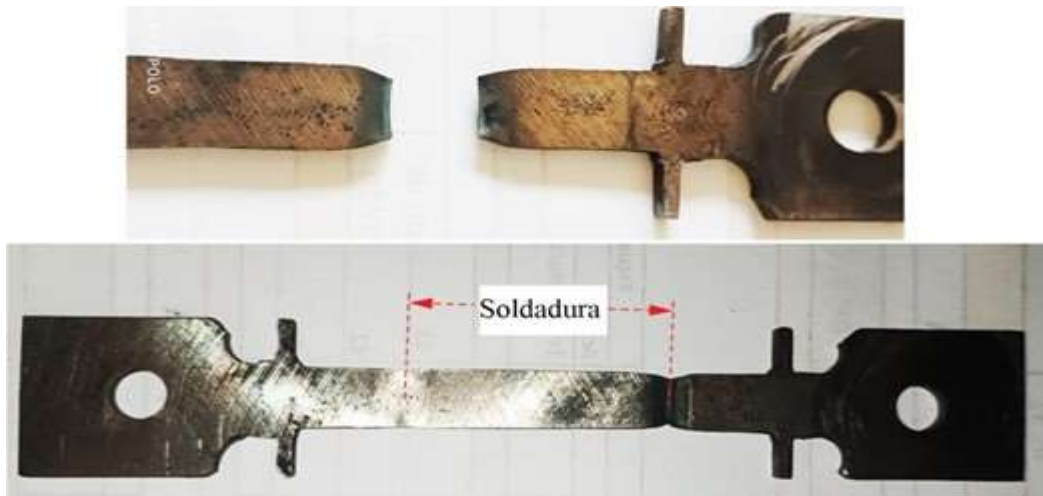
Tratamiento térmico post soldadura de 3 h a 730°C
